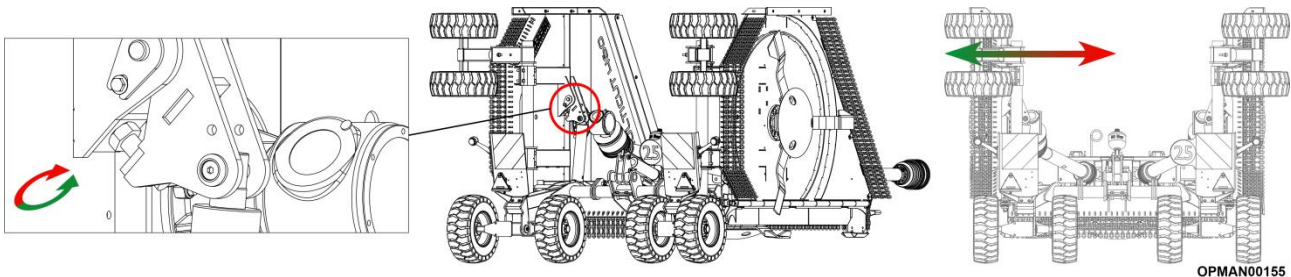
Multicut 460 Регулировка транспортной ширины
